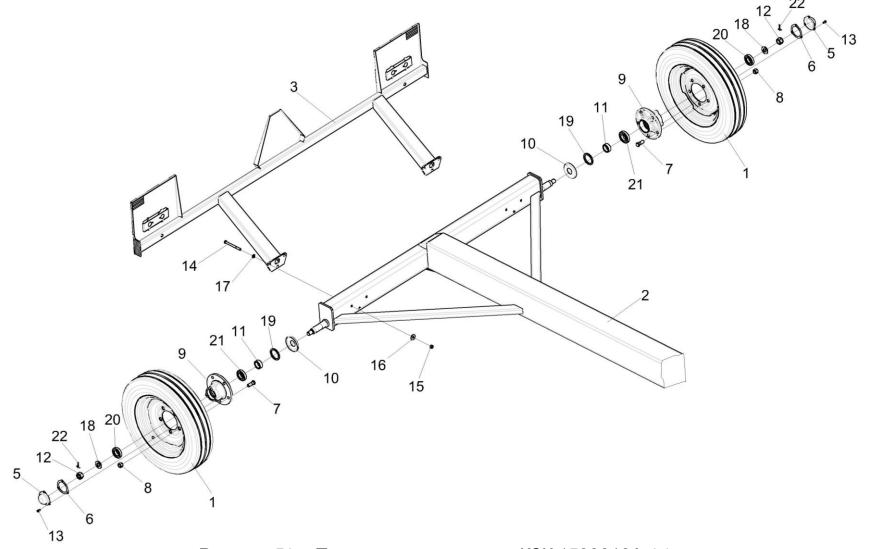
Тележка транспортная КЗК 1590010A-04 (установка задних колес и балки габаритной)
